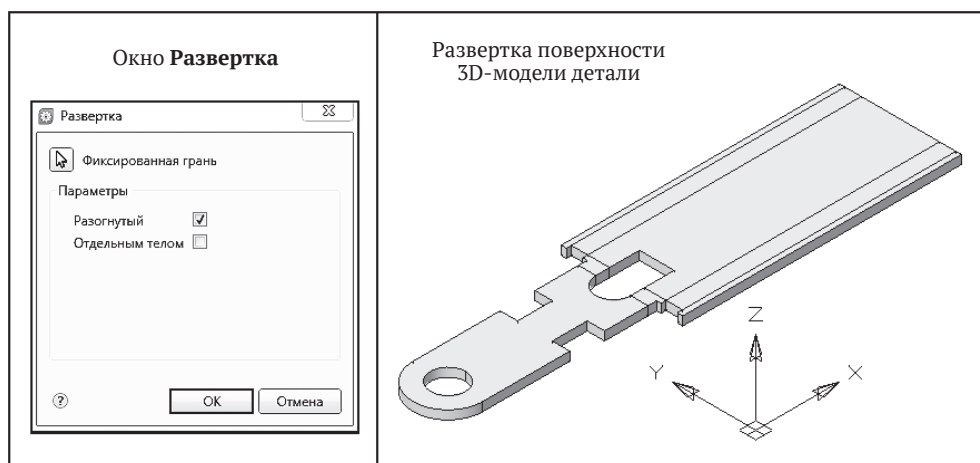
Пример построения развертки поверхности 3D-модели детали «Кронштейн»
